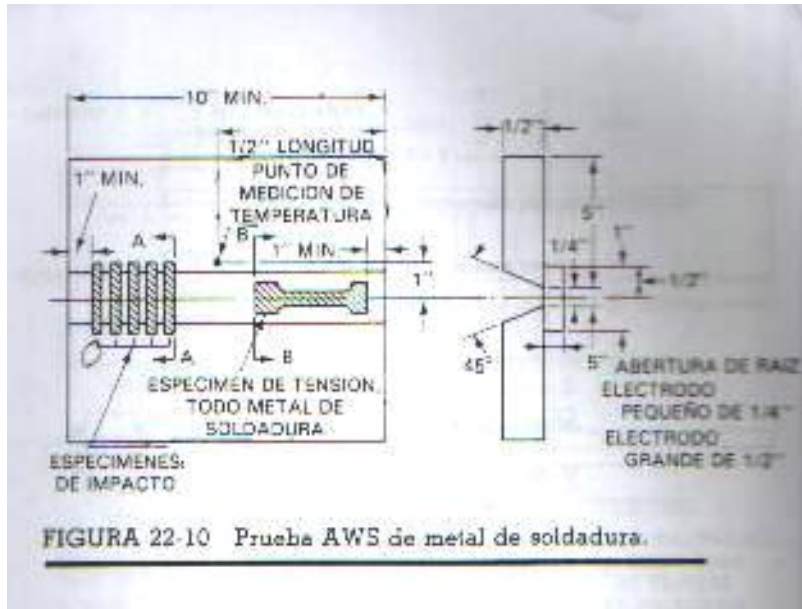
Prueba AWS de metal de soldadura.
